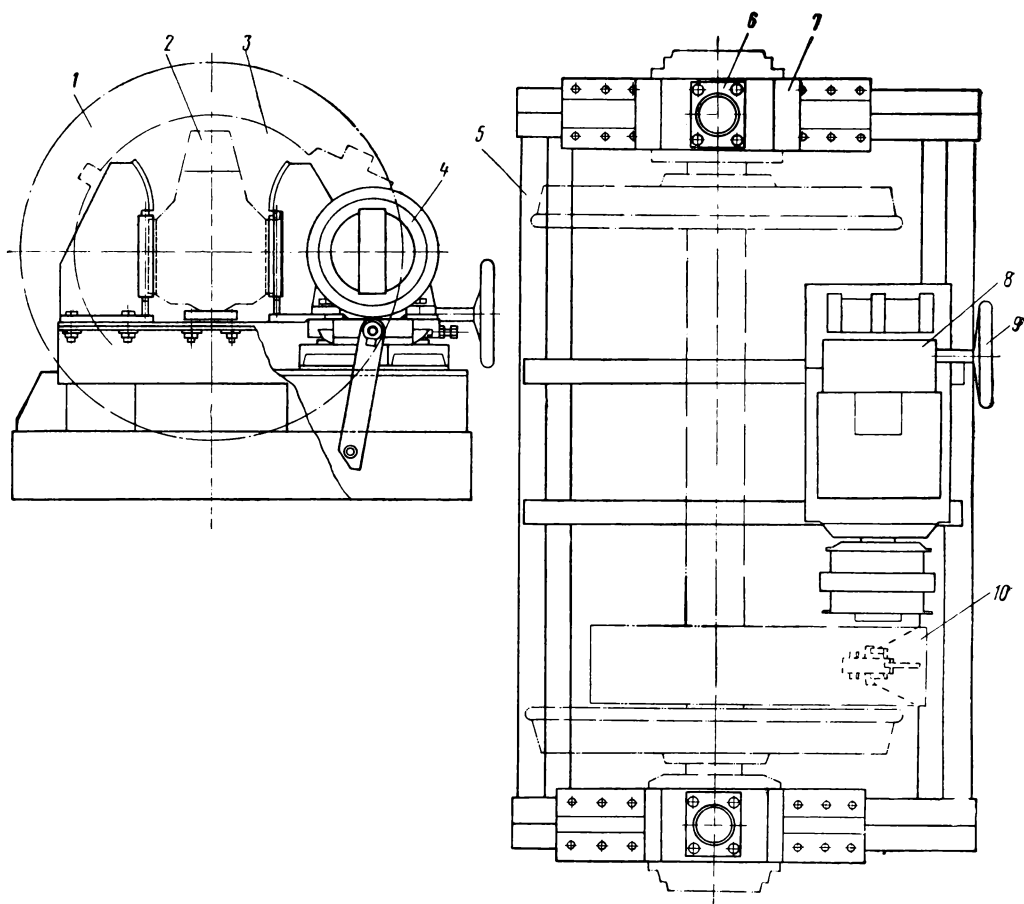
Стенд для обкатки колесной пары с редуктором:
